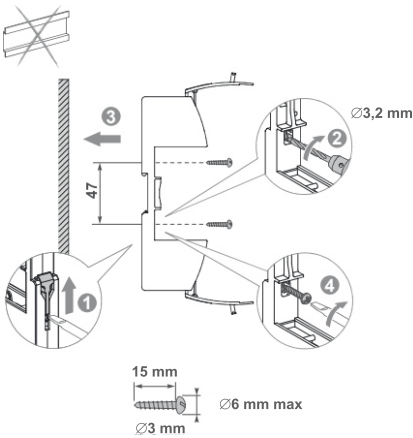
Монтаж модуля на монтажную панель / Figure 4 – Mounting the module on a mounting panel
